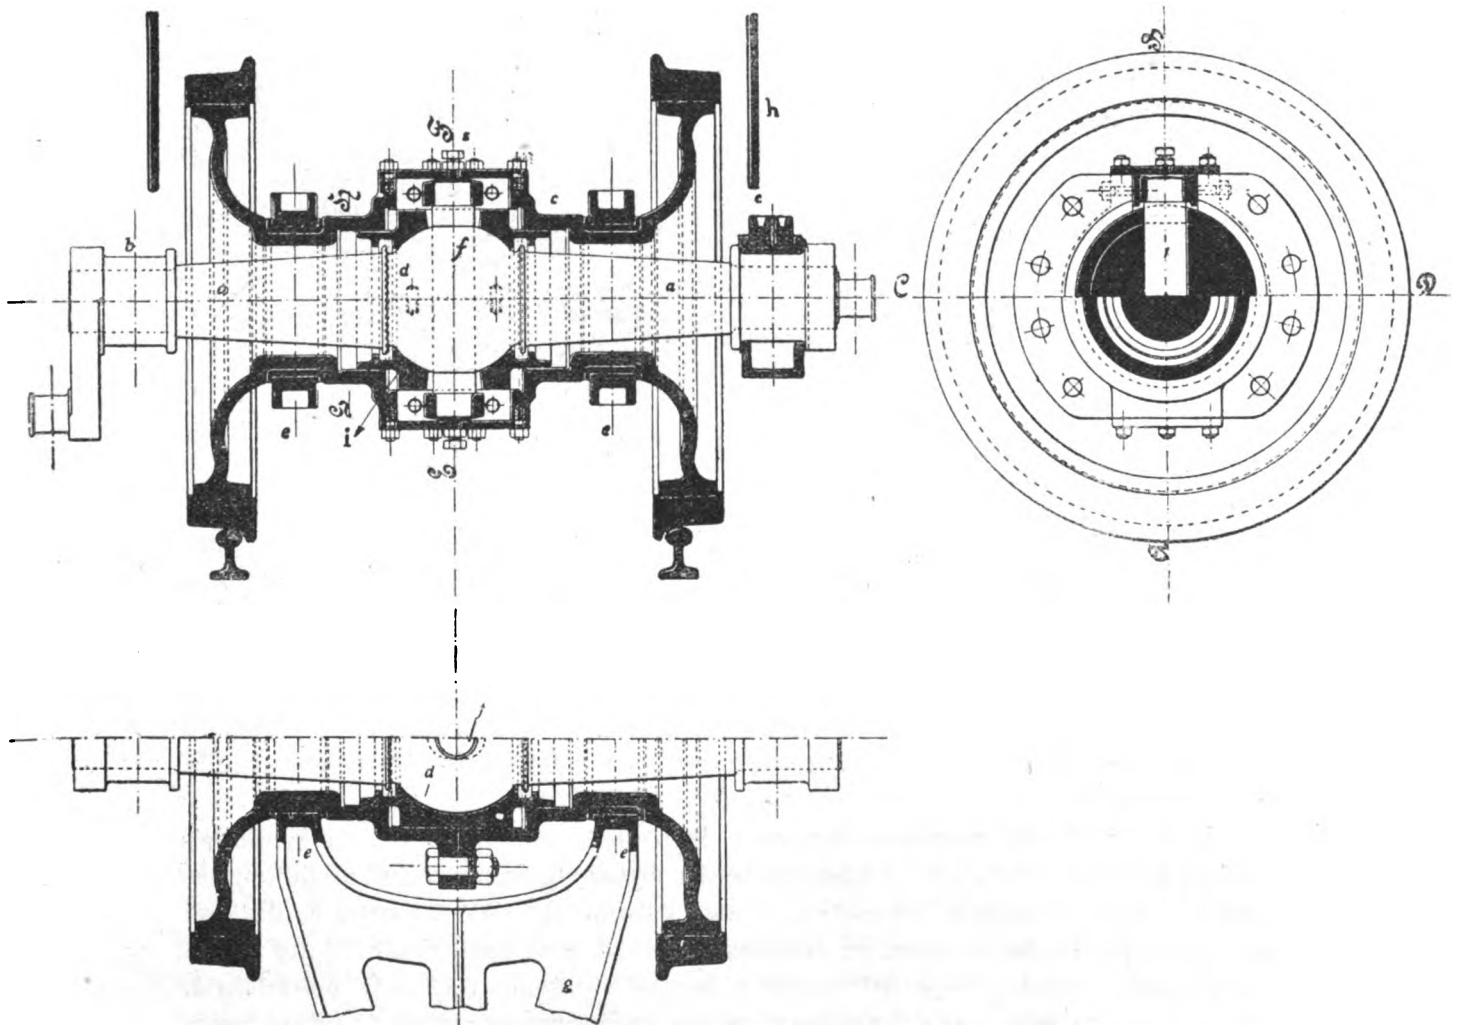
Tipo di asse cave sistema Klien-Lindner.
